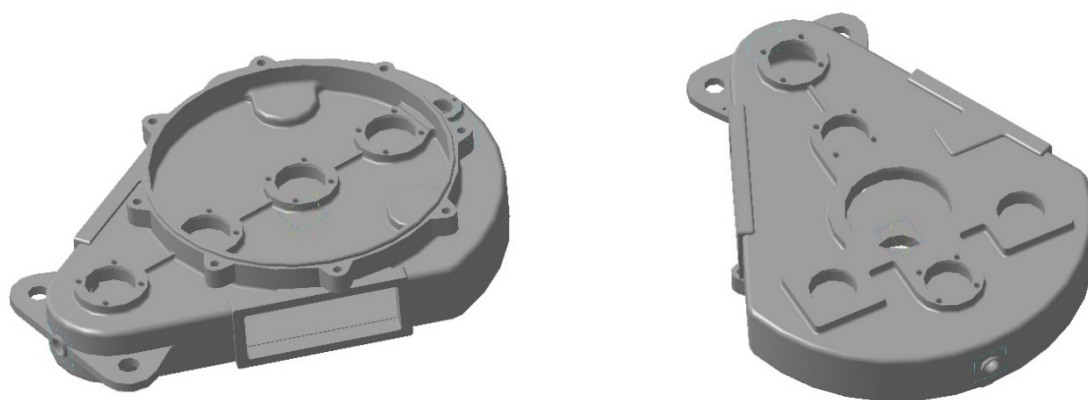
3D-модель детали «Корпус цилиндрического редуктора»
